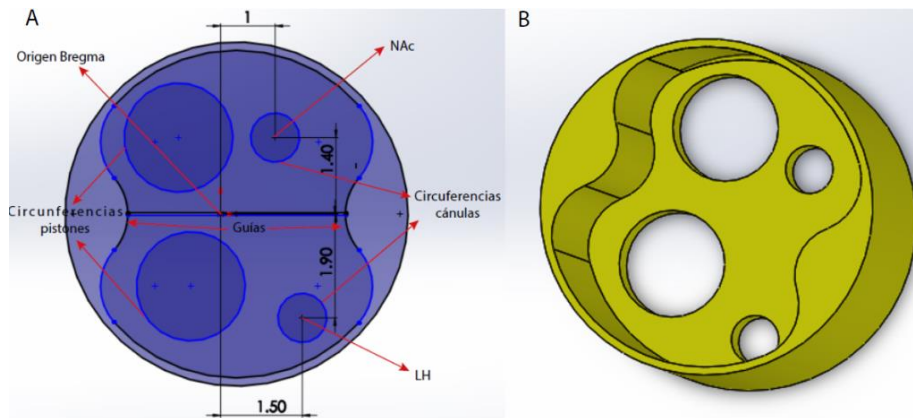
Diseño buje. (A) Croquis de diseño. (B) CAD del buje.
